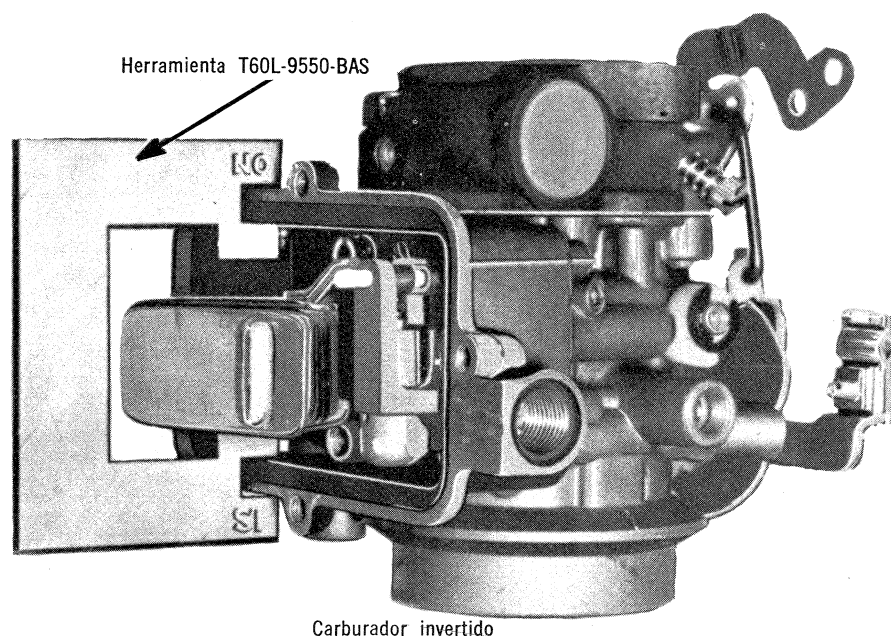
Control de la Altura del Flotante Carburador Desmontado.
